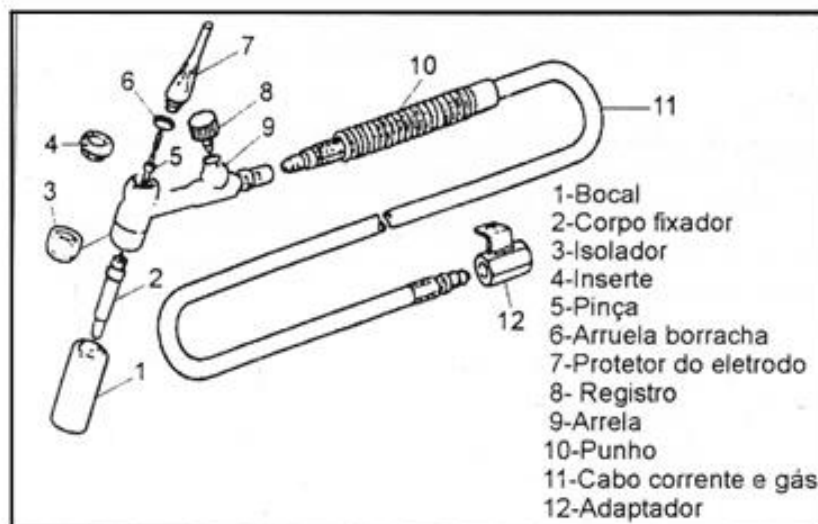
Representação esquemática de uma tocha para soldagem TIG.
